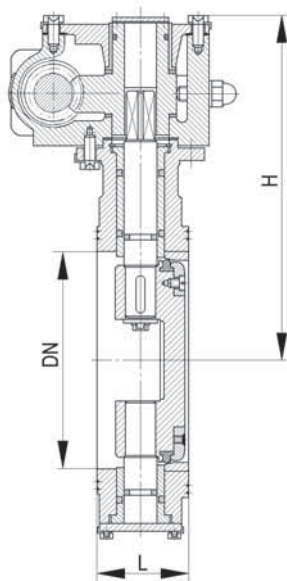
Затвор поворотный с ручным приводом
